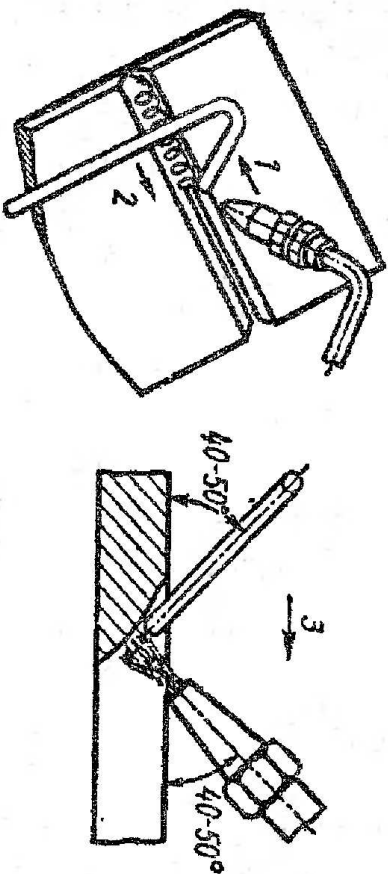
Правый способ пайкосварки. 1 — движение горелки; 2 — движение прутка; 3 — движение горелки и прутка
